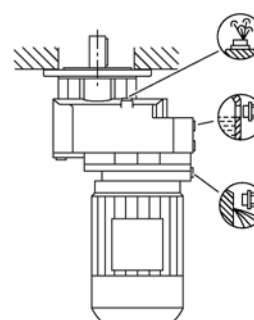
Монтажные положения для цилиндрического редуктора E в исполнении на лапах, типоразмеры 39 - 149
